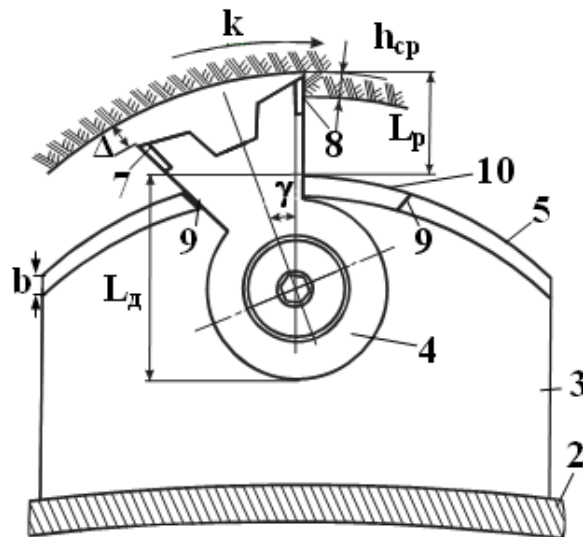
Разрушение забоя реверсивным двухлезвийным поворотным резцом
